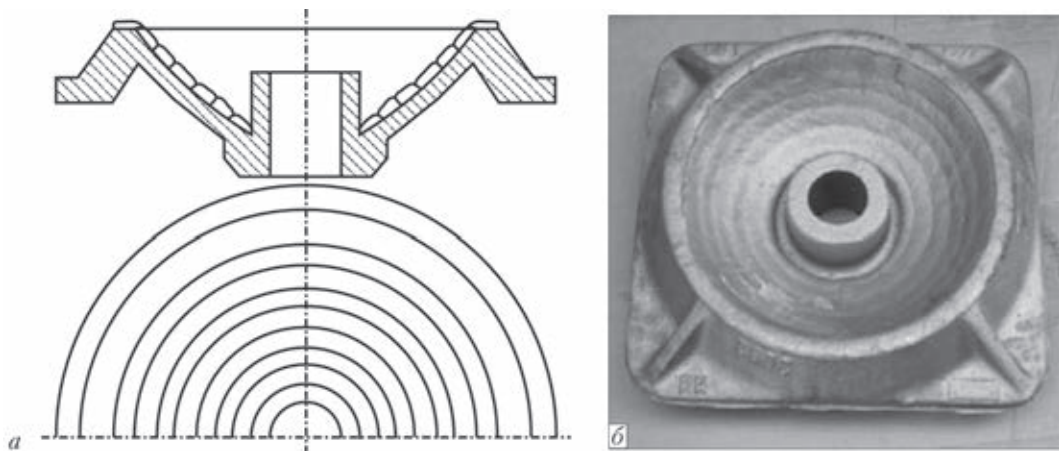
Схема литого гнезда поворота из стали 45Л (наружный диаметр 380 мм, толщина стенки 32 мм): схема (а) и внешний вид наплавленной детали (б) (толщина наплавленного слоя 9,0...13,0 мм)
